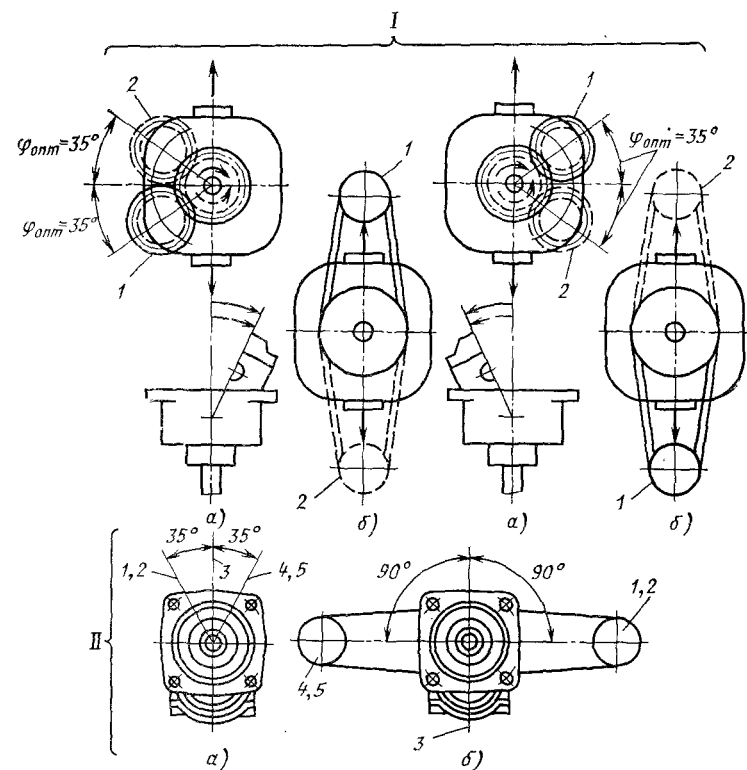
Схема выбора оптимального угла установки зубчатой (а) и клиноременной (б) передачи для гидромашин типа 207 (I) и 210 (II):
